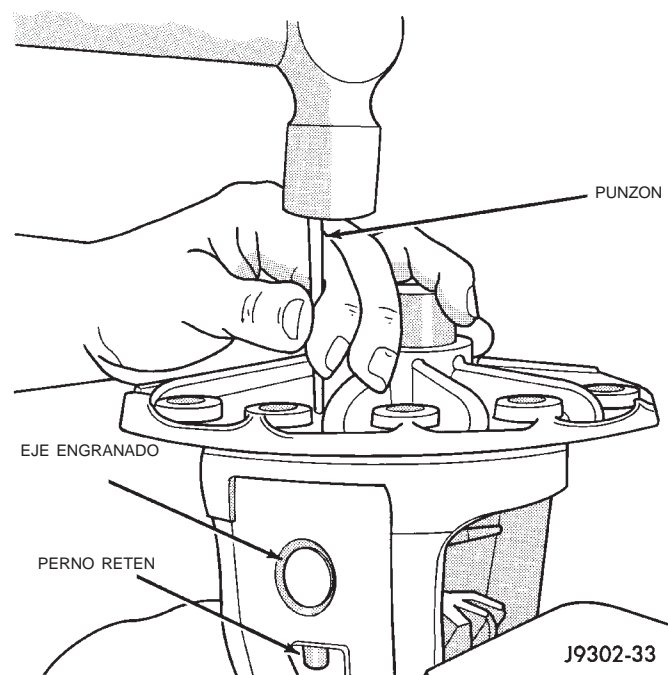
Desmontaje del pasador de rodillo del eje engranado
